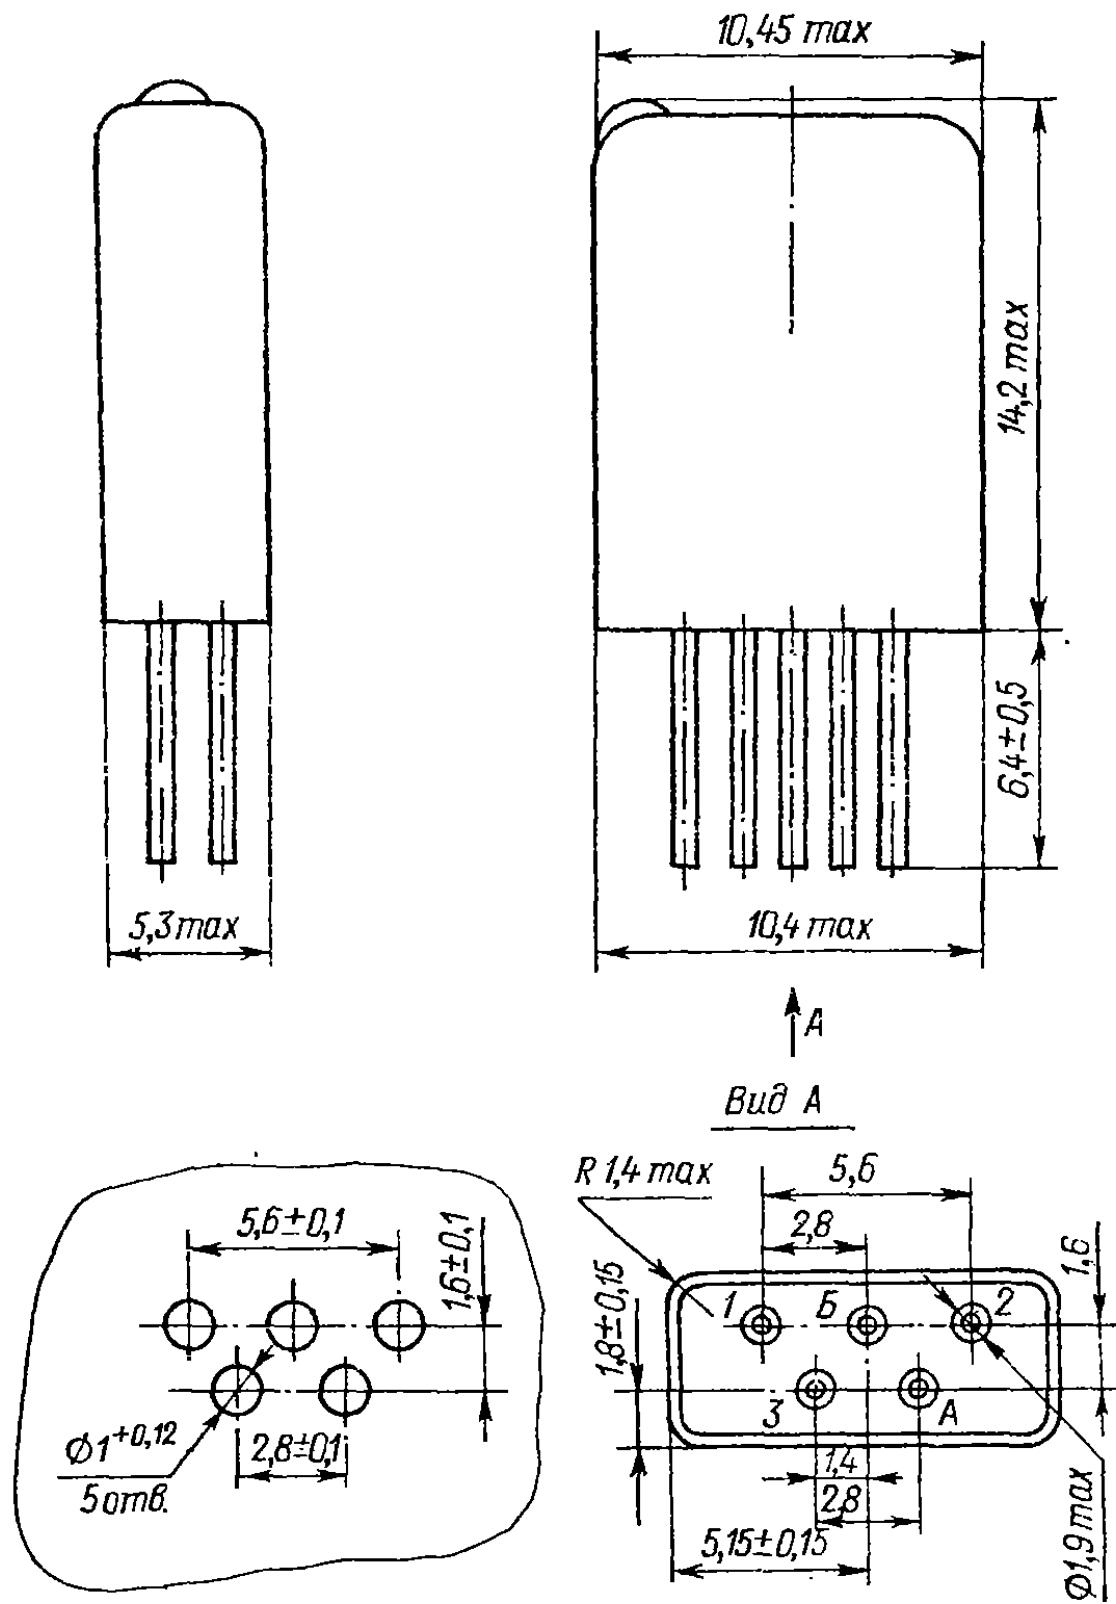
Конструктивные данные реле РЭК23, маркировка и разметка для крепления
